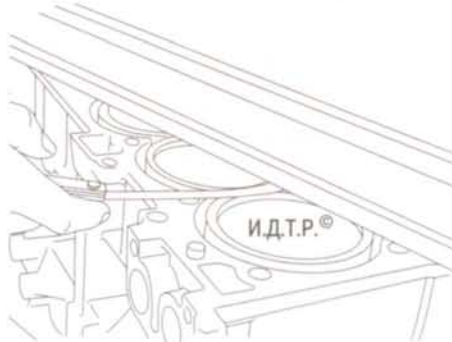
Проверка плоскостности привалочной поверхности блока цилиндров двигателя
